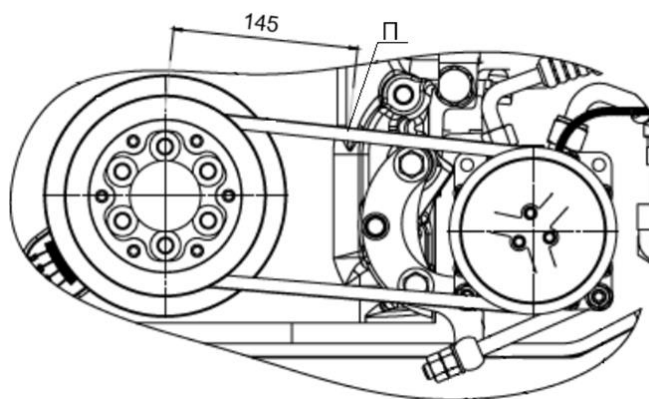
Регулировка ремня привода компрессора, установленного на двигателе
